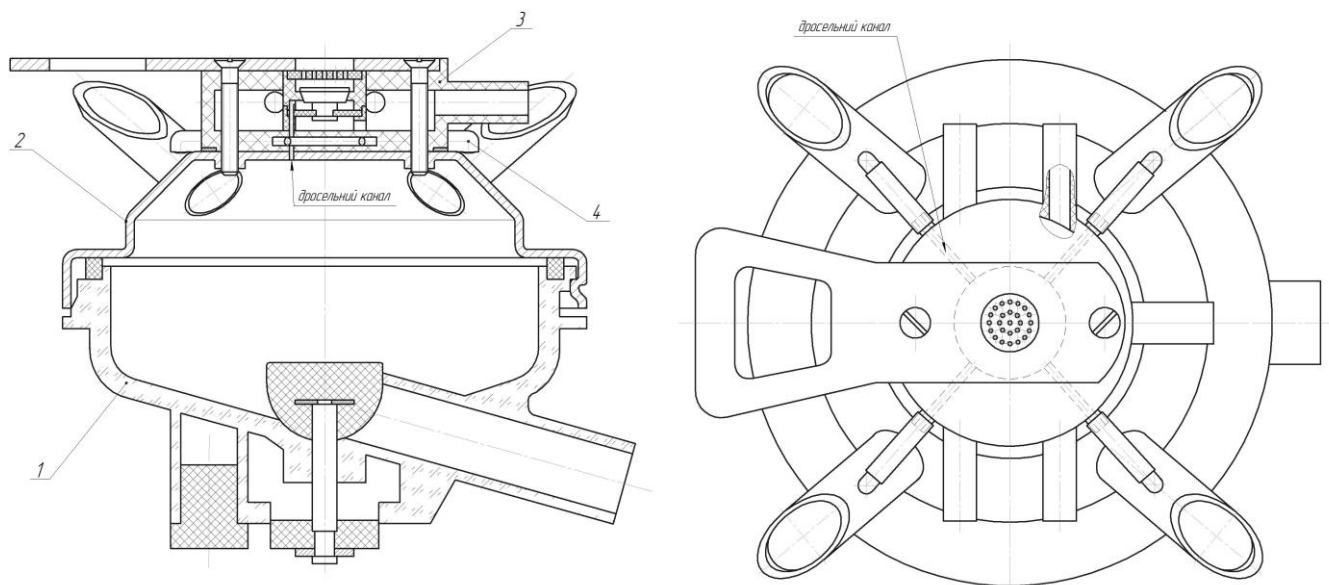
Загальний вигляд розробленого колектора доїльного апарата: 1 – корпус молочного простору; 2 – корпус; 3 – корпус розподільника; 4 – патрубок з'єднувальний.
